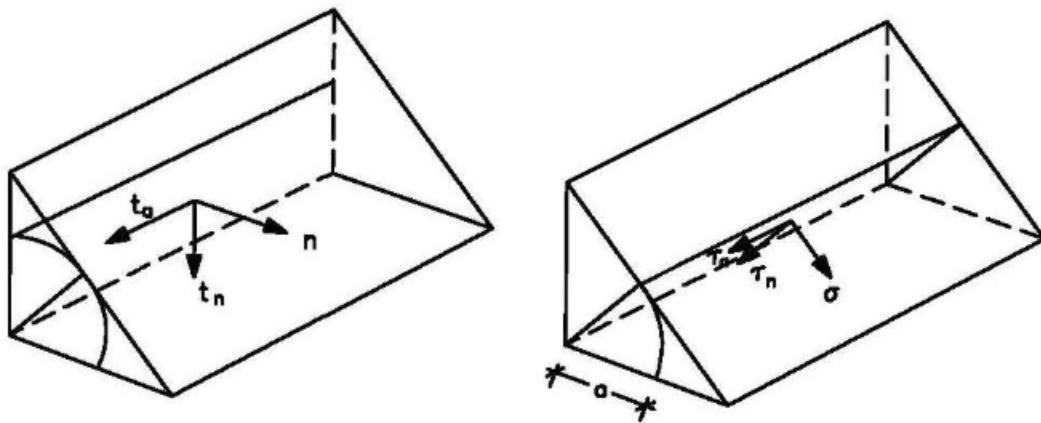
Esquema traslado de las tensiones del plano de garganta al lado del cordón.
